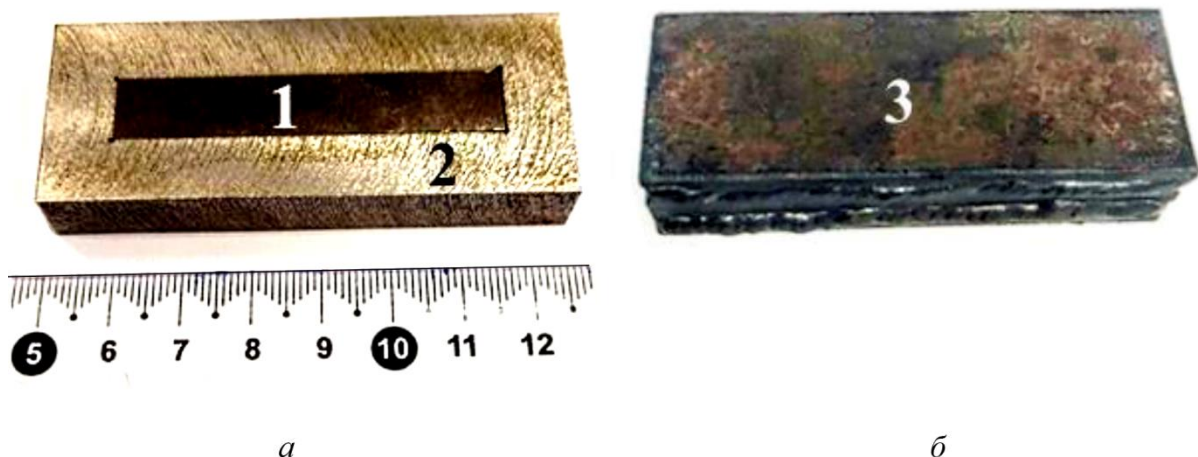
Внешний вид запрессованного образца (а) и закрытой стальной оболочки (б):
